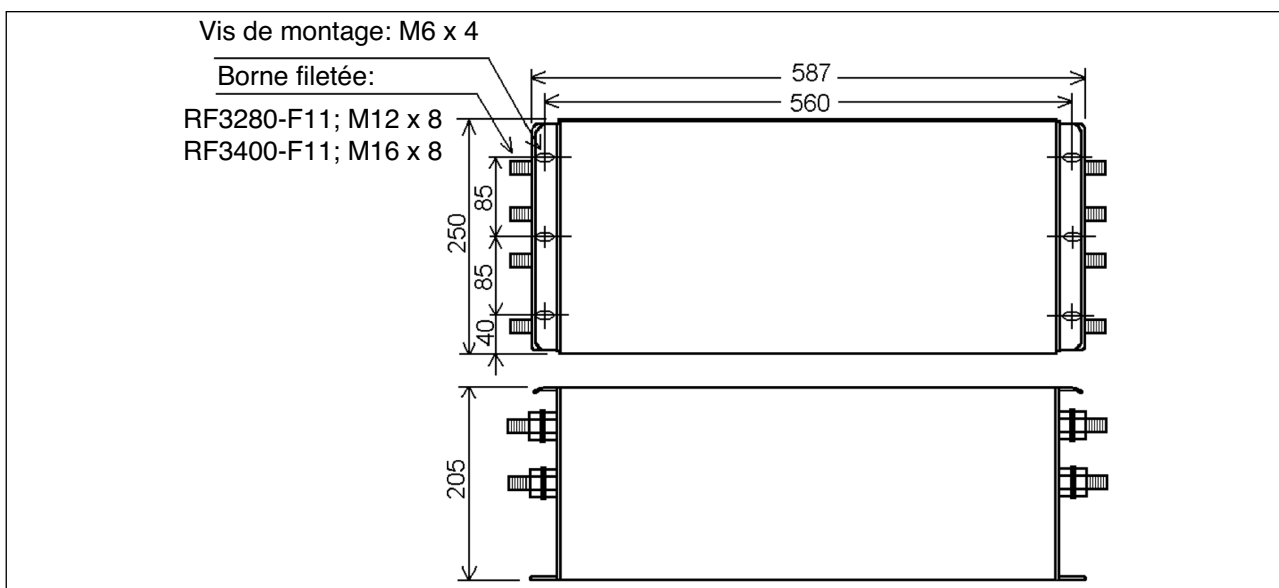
Dimensions externes (RF3280-F11, RF3400-F11)
